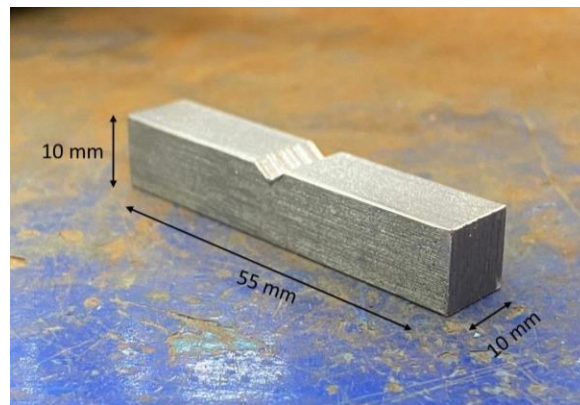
Dimensiones de la probeta de impacto Charpy. Fuente propia
